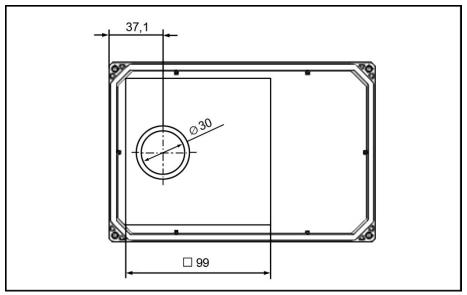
Bohrbild Standard-Adapterplatte BG a
